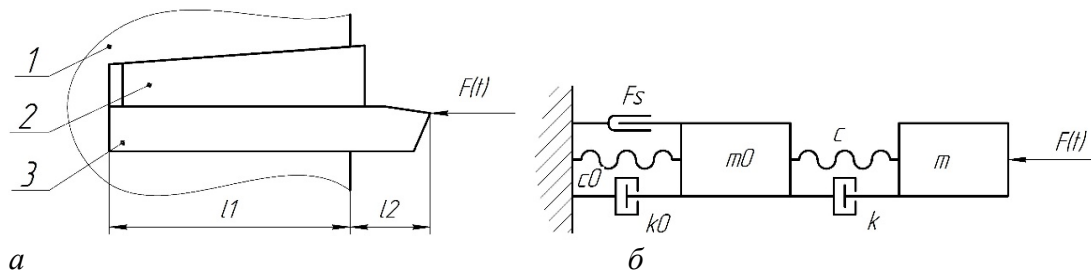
Конструктивна (а) та розрахункова (б) схеми пресового з'єднання
